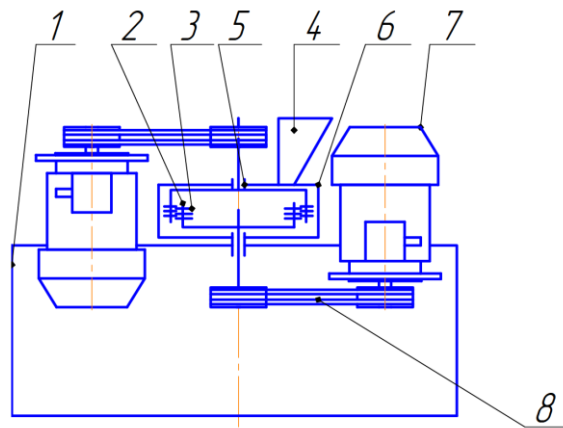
Дробарка ударно-відцентрова: 1 – рама; 2 – ротор; 3 – елемент подрібнювальний; 4 – бункер приймальний; 5 – опора; 6 – кришка; 7 – електродвигун; 8 – передача ремінна.
